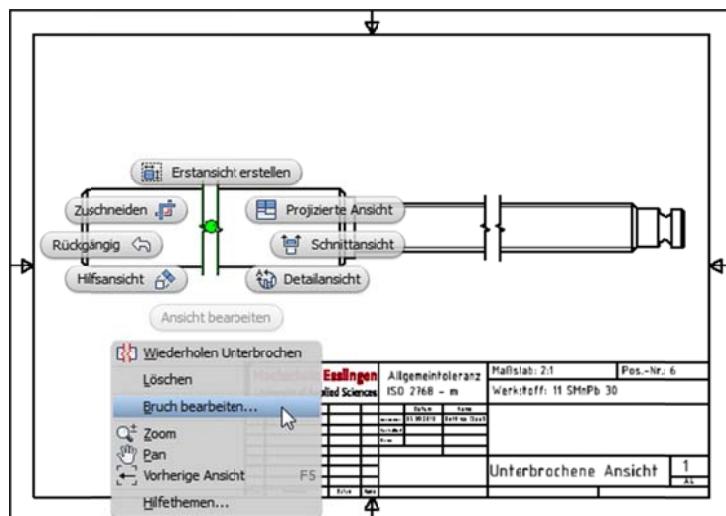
Bearbeitung unterbrochener Ansichten.
